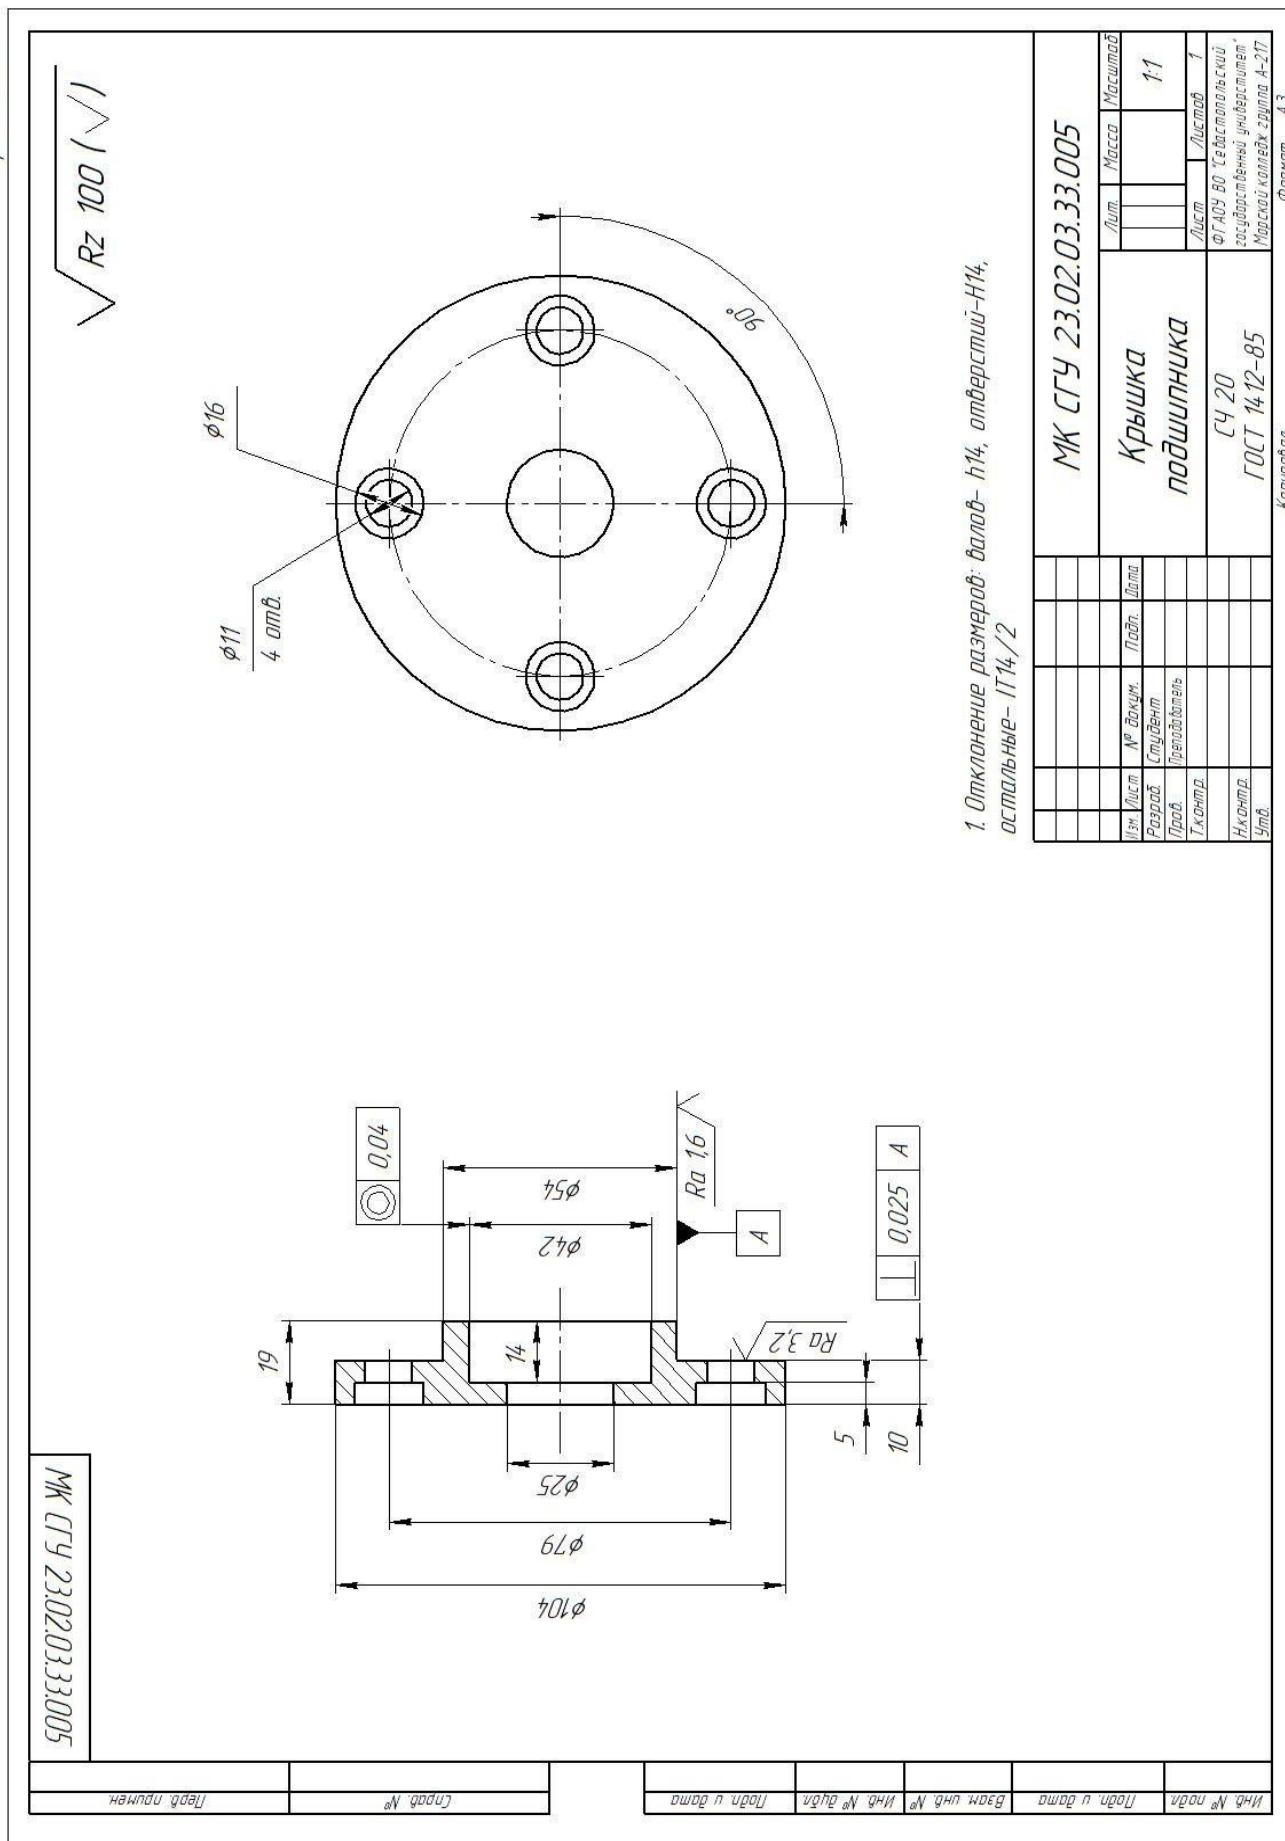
Пример выполненного чертежа детали крышка подшипника
